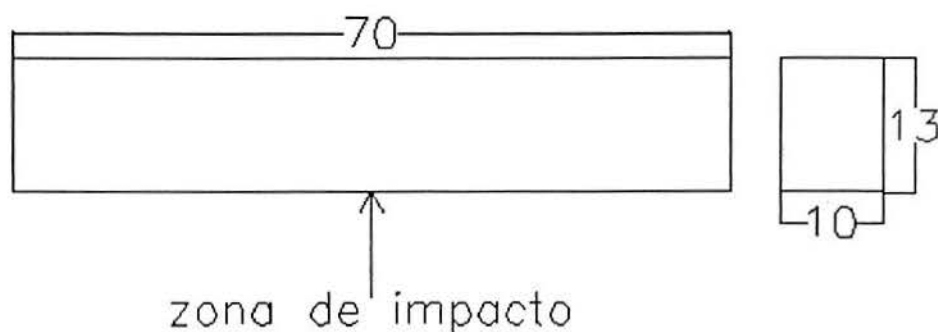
Dimensões do corpo de prova utilizado para impacto com pêndulo de Charpy, dimensões em mm.
